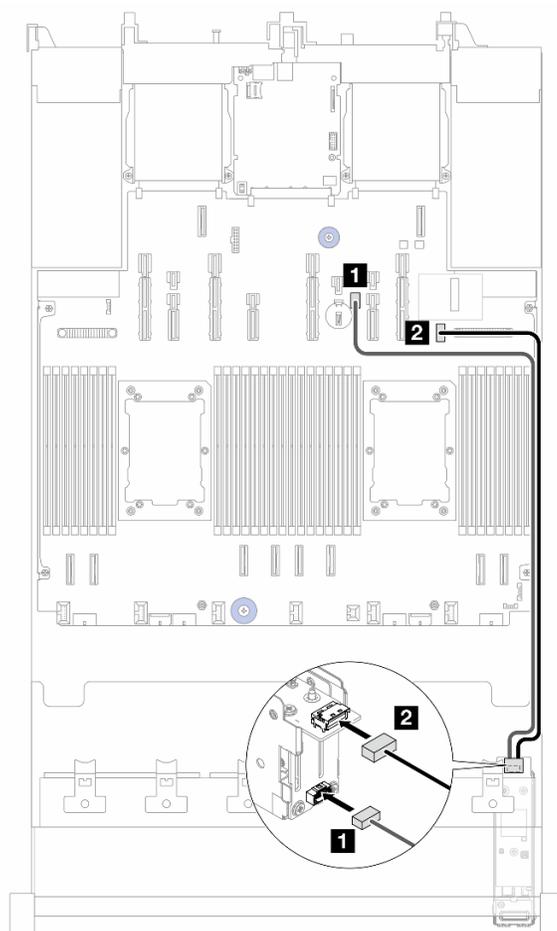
Disposición de los cables para la placa posterior de arranque y la placa controladora M.2 frontal
